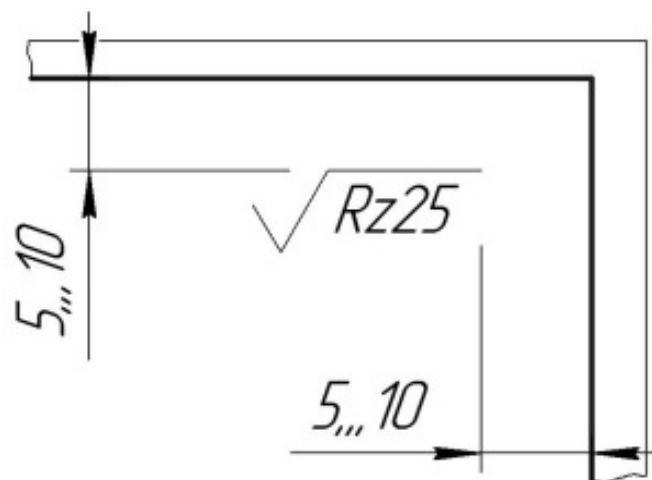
Указание шероховатости одинаковой для всех поверхностей изделия
